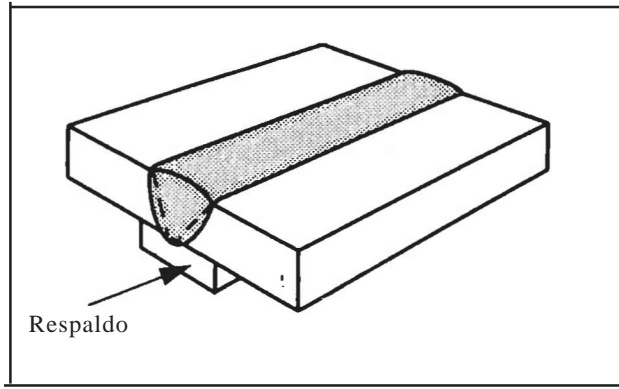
SOLDADURA CON RESPALDO
